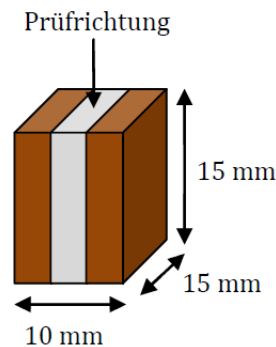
Maße einer Spaltprobe laut DIN 53463
